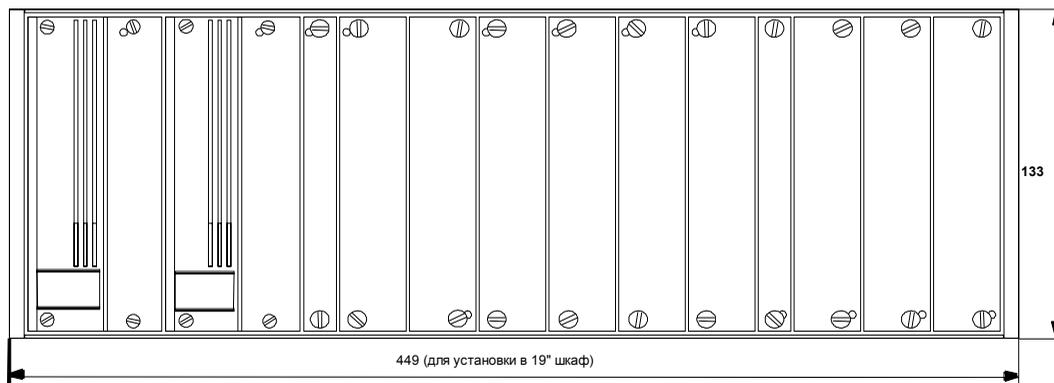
Активный звездообразный разветвитель ASGE (вид спереди; габариты в мм)
